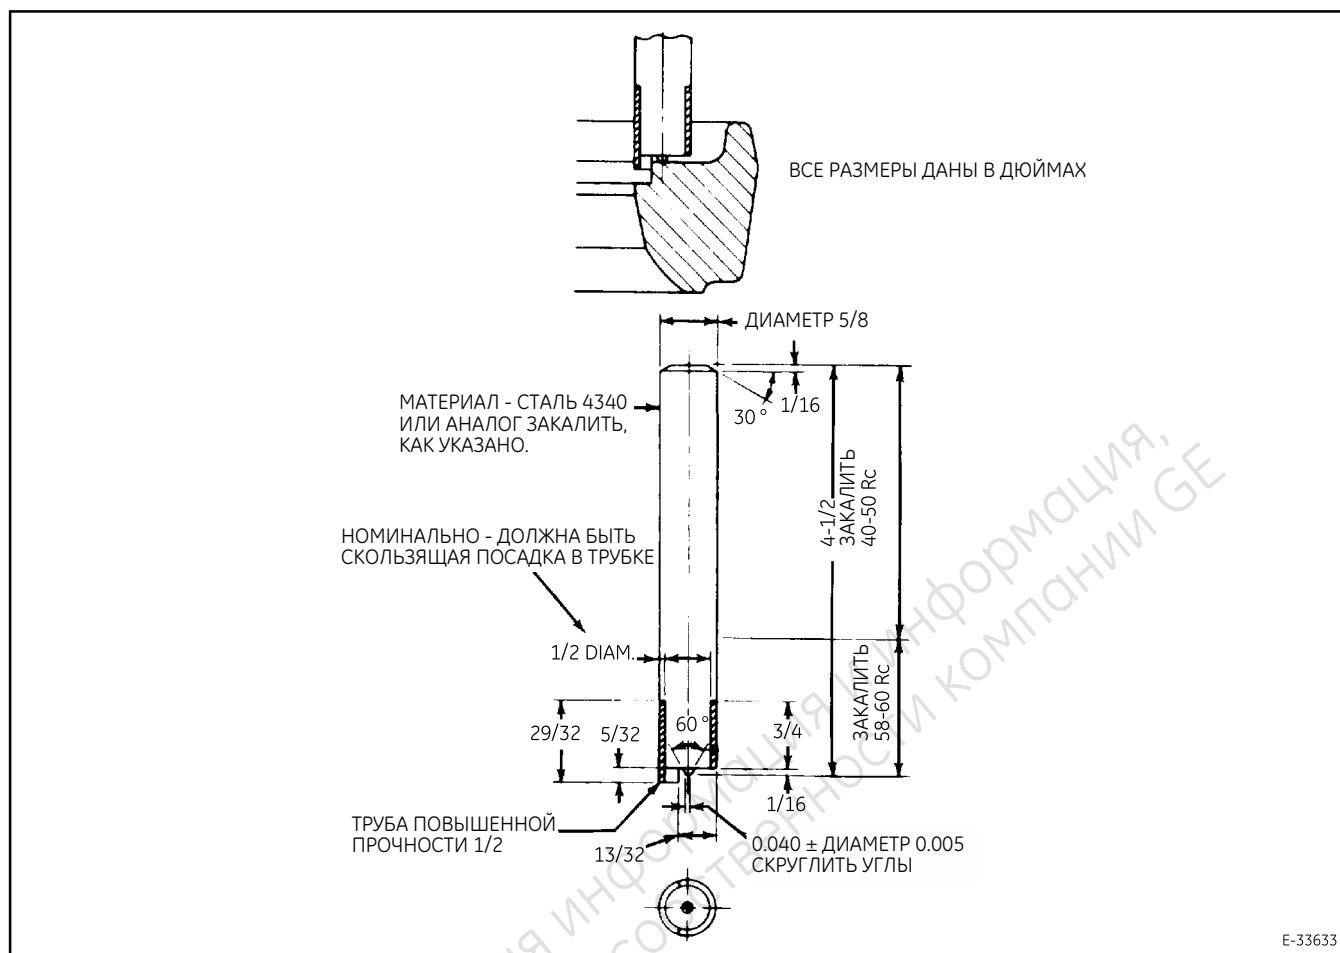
Ремонтное кернение торцевой расточки упорного кольца.
